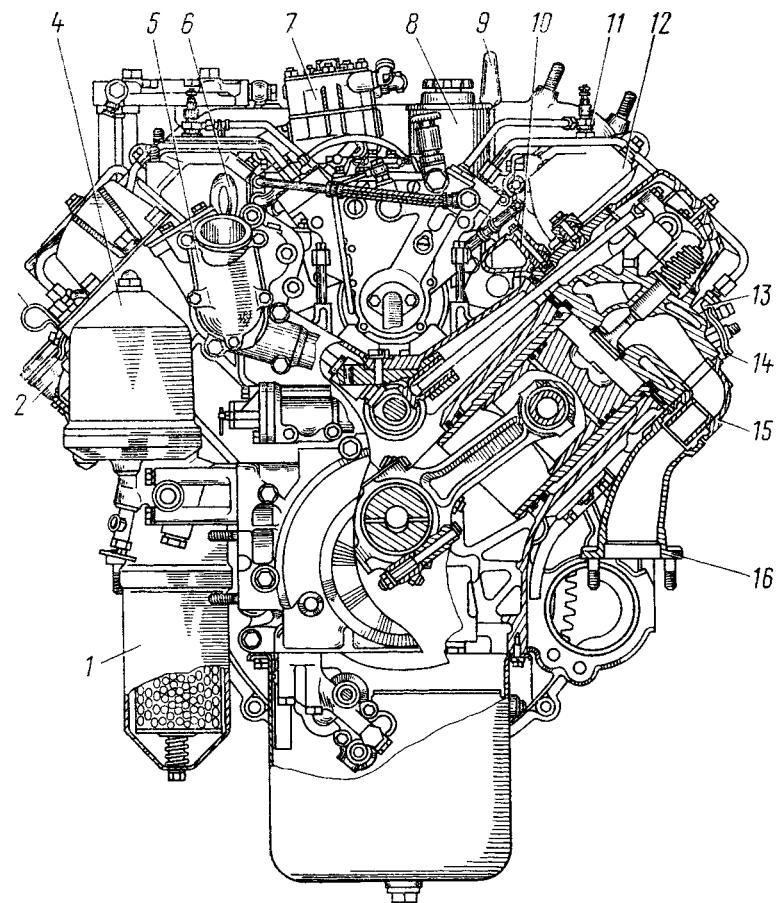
Поперечный разрез двигателя КамАЗ-740.10: 1 - фильтр полнопоточный очистки масла; 2 - горловина маслозаливная; 3 - указатель уровня масла; 4 - фильтр центробежный масляный; 5 - коробка термостатов; 6 - рым-болт передний; 7 - компрессор; 8 - насос гидроусилителя рулевого управления; 9 - рым-болт задний; 10 - труба водяная левая; 11 - свеча факельная; 12-воздухопровод выпускной левый; 13 - форсунка; 14 - скоба крепления форсунки; 15 - патрубок выпускного коллектора; 16 - коллектор выпускной
